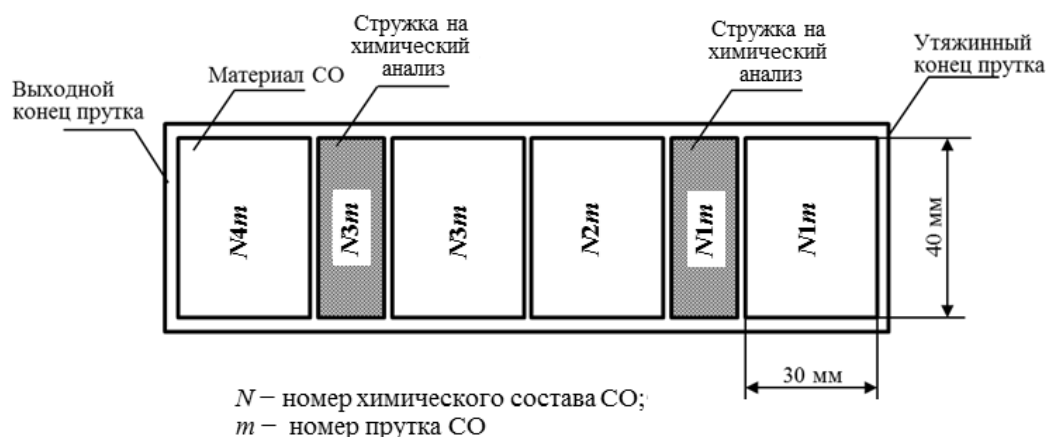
Схема разрезки заготовки стандартного образца (СО)
